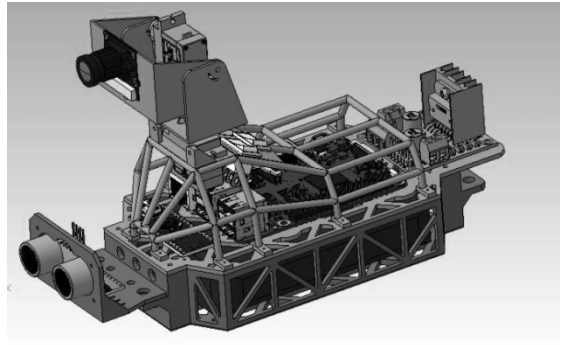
Загальний вигляд зборки блоку управління з розміщеними компонентами
